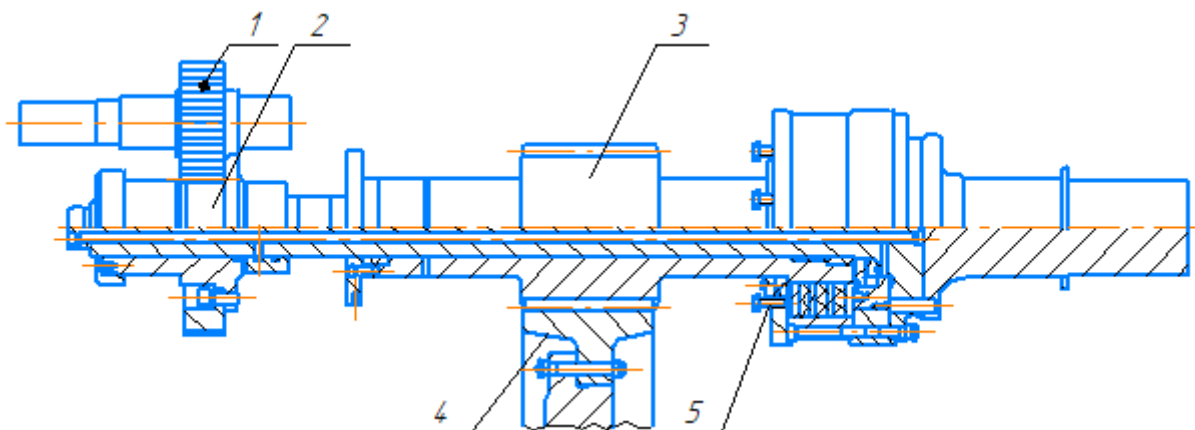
Ведучий вал з муфтою зчеплення: 1 – зубчасте колесо; 2 – механізм відбору потужності; 3 – шестерня головної передачі; 4 – зубчасте колесо головної передачі; 5 – фіксує болт
